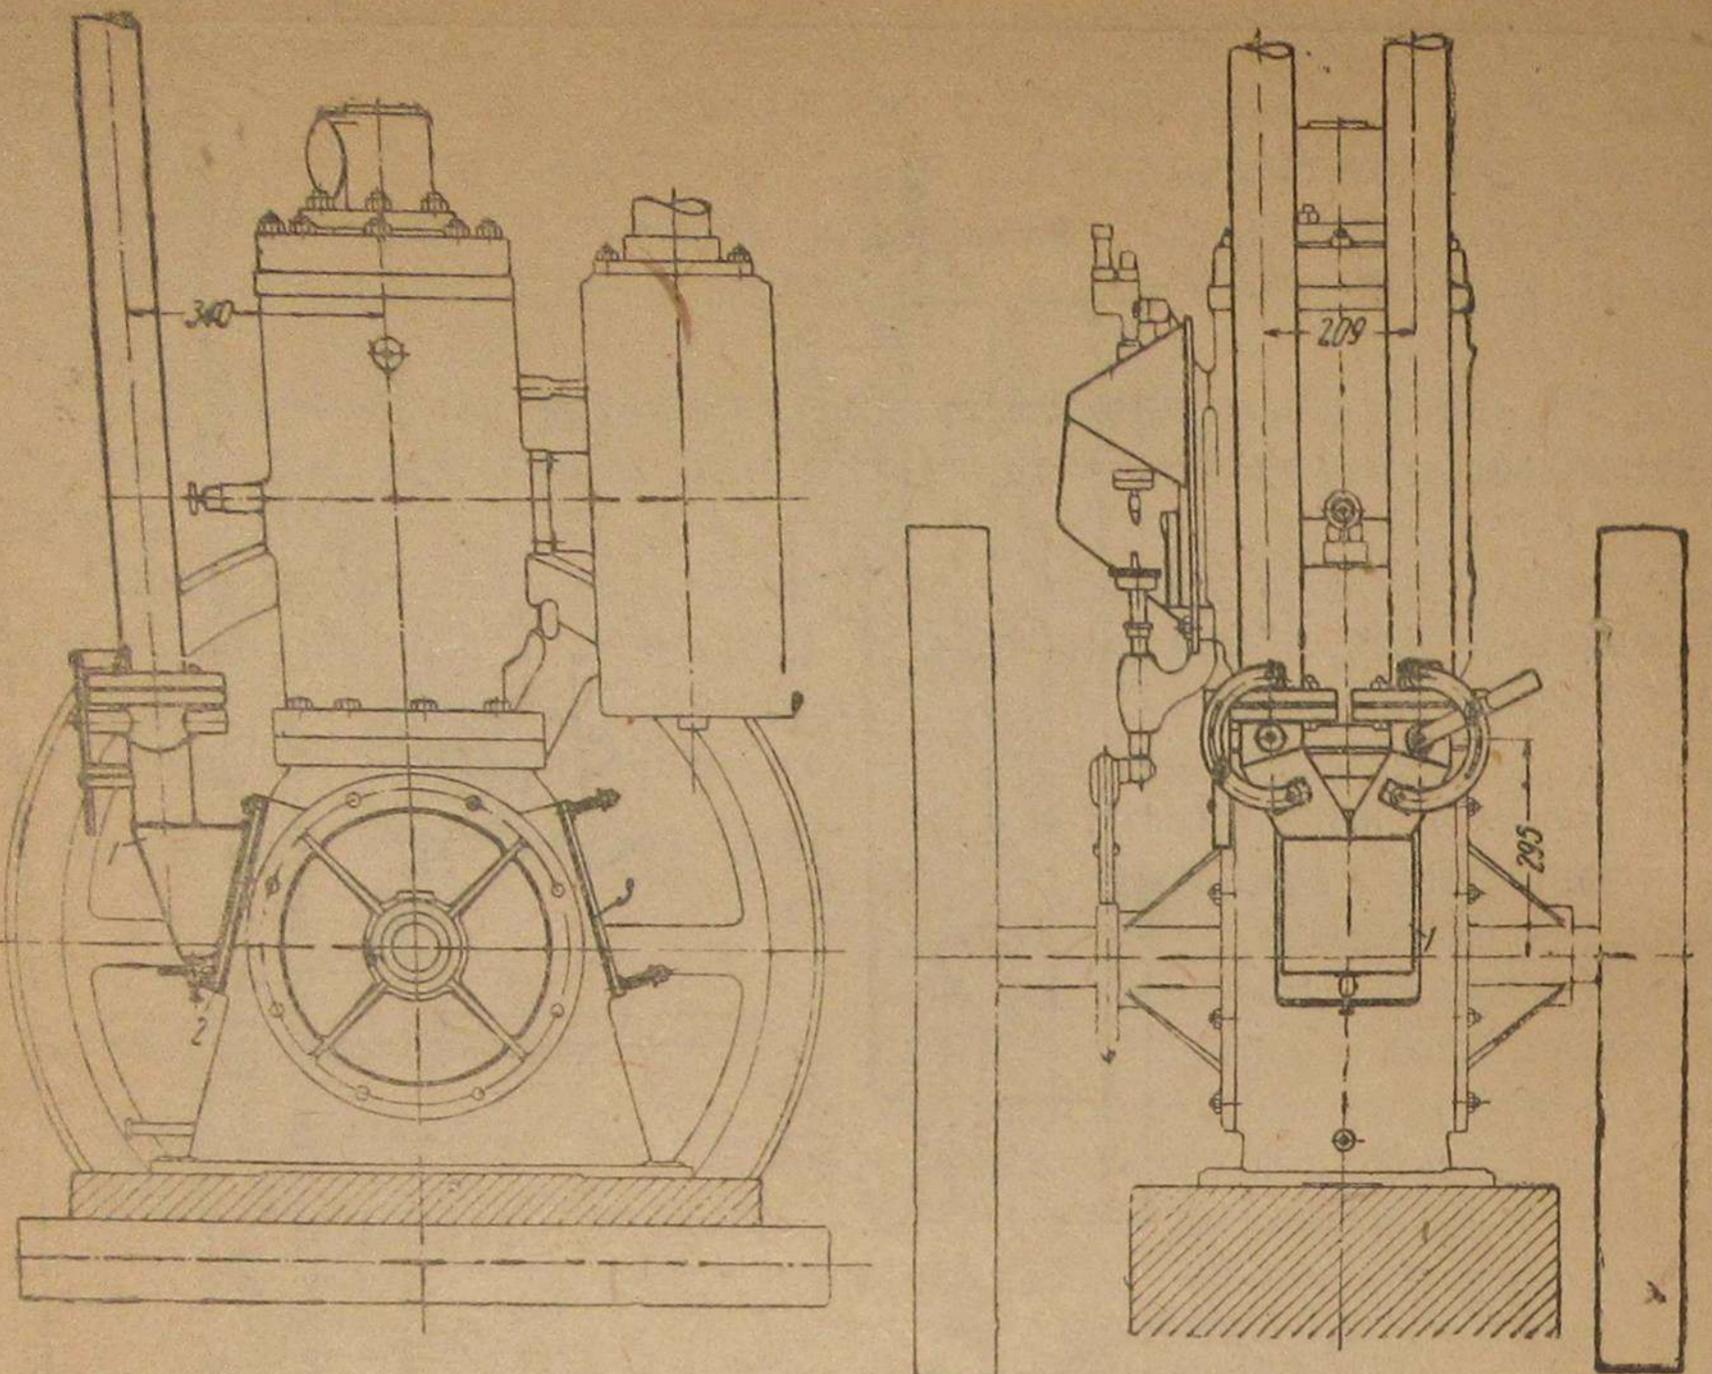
Общий вид двигателя мощностью 18 л. с., переведённого на газ:
